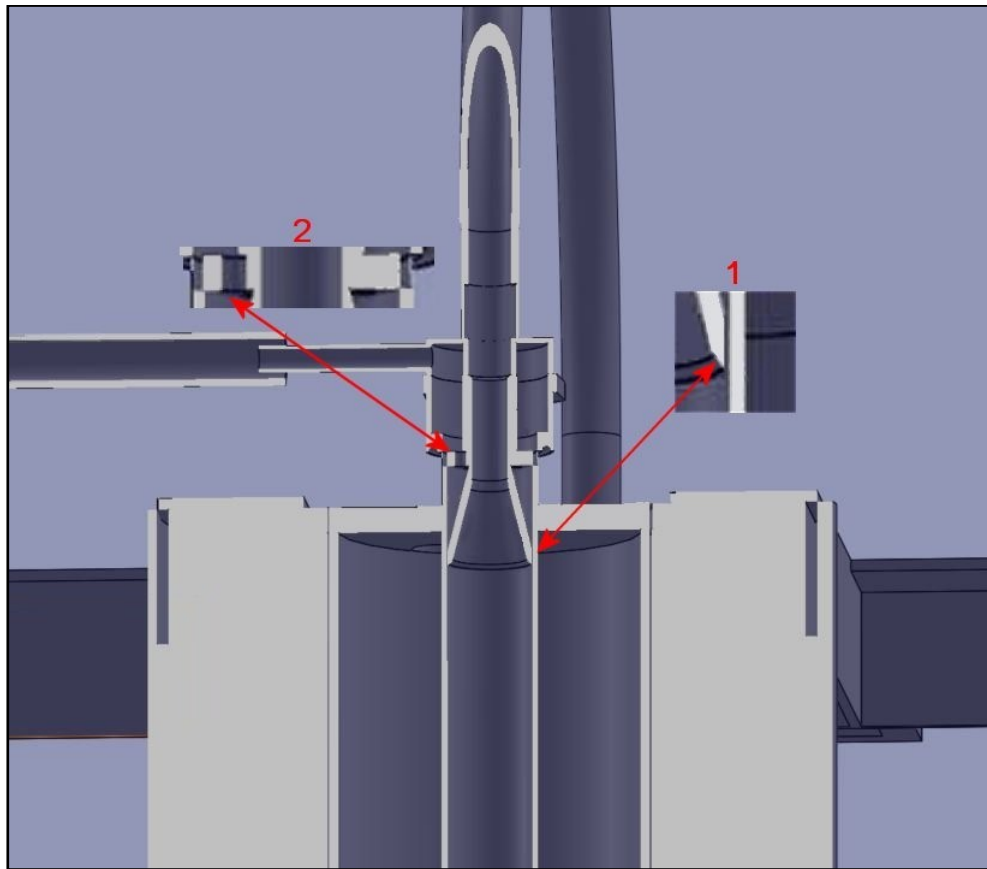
SDA instalado. em (a) detalhe do cone; em (b) vista completa
